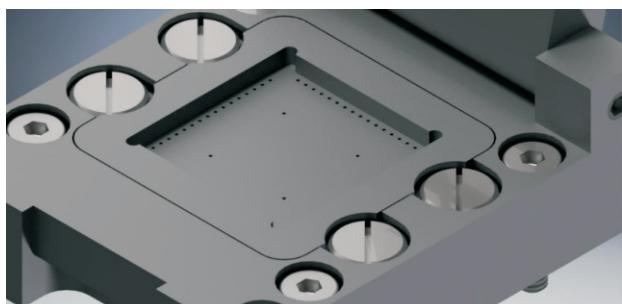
Внешний вид КУ для без выводных корпусов (со скрытием контактов)
